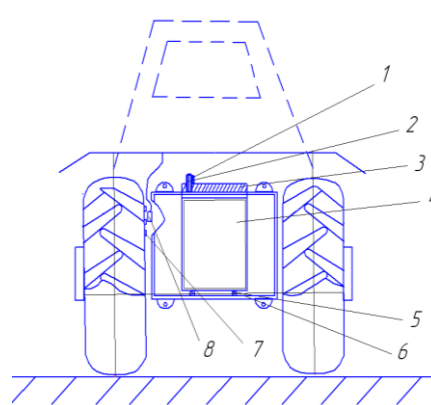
Принципиальная схема трактора, оборудованного весовым догрузителем с автоматическим перемещением массы: 1 – зубчатая рейка передаточного механизма гидrocилиндра; 2 – приводная шестерня передаточного механизма; 3 – зубчатая рейка съёмного бака; 4 – съёмный бак с жидкостью; 5 – обрезиненные ролики; 6 – рама с кронштейнами для крепления на тракторе; 7 – корона; 8 – индуктивный датчик
